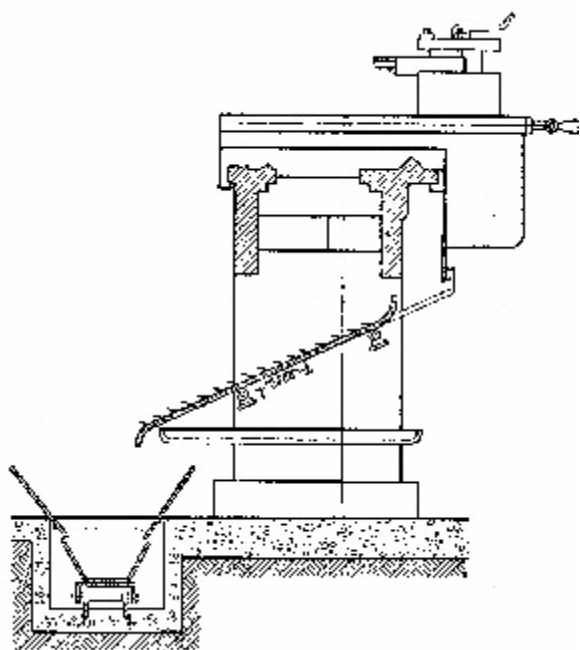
Схема устройства скребкового типа для уборки стружки из рабочей зоны станка
